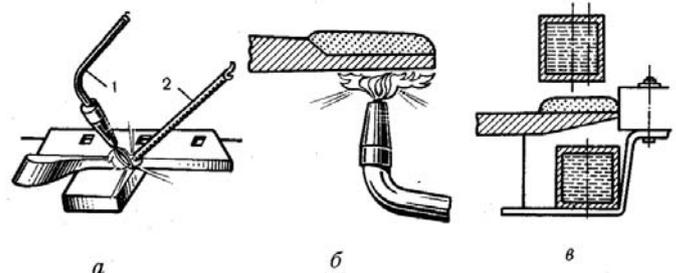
Способы нагрева лезвия плужного лемеха при наплавке твердого сплава: а — прямой нагрев прутка из твердого сплава «Сормайт-1» газовой горелкой; б — нижний нагрев лезвия с насыпной шихтой; в — нагрев токами высокой частоты; 1 — горелка; 2 — пруток из твердого сплава
